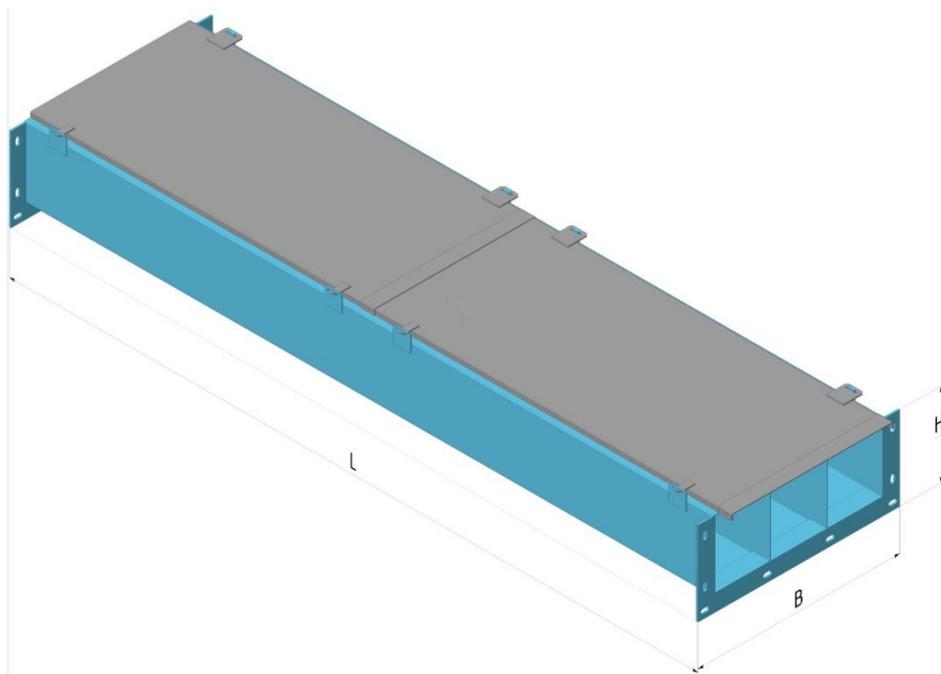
Короб кабельный блочный прямой плоский типа ККБ-ПО. Общий вид. Крышка с креплением на защелки, две крышки длиной 1 м каждая.
